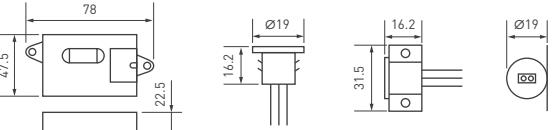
Габаритные размеры ИК-датчика SR-PRIME
